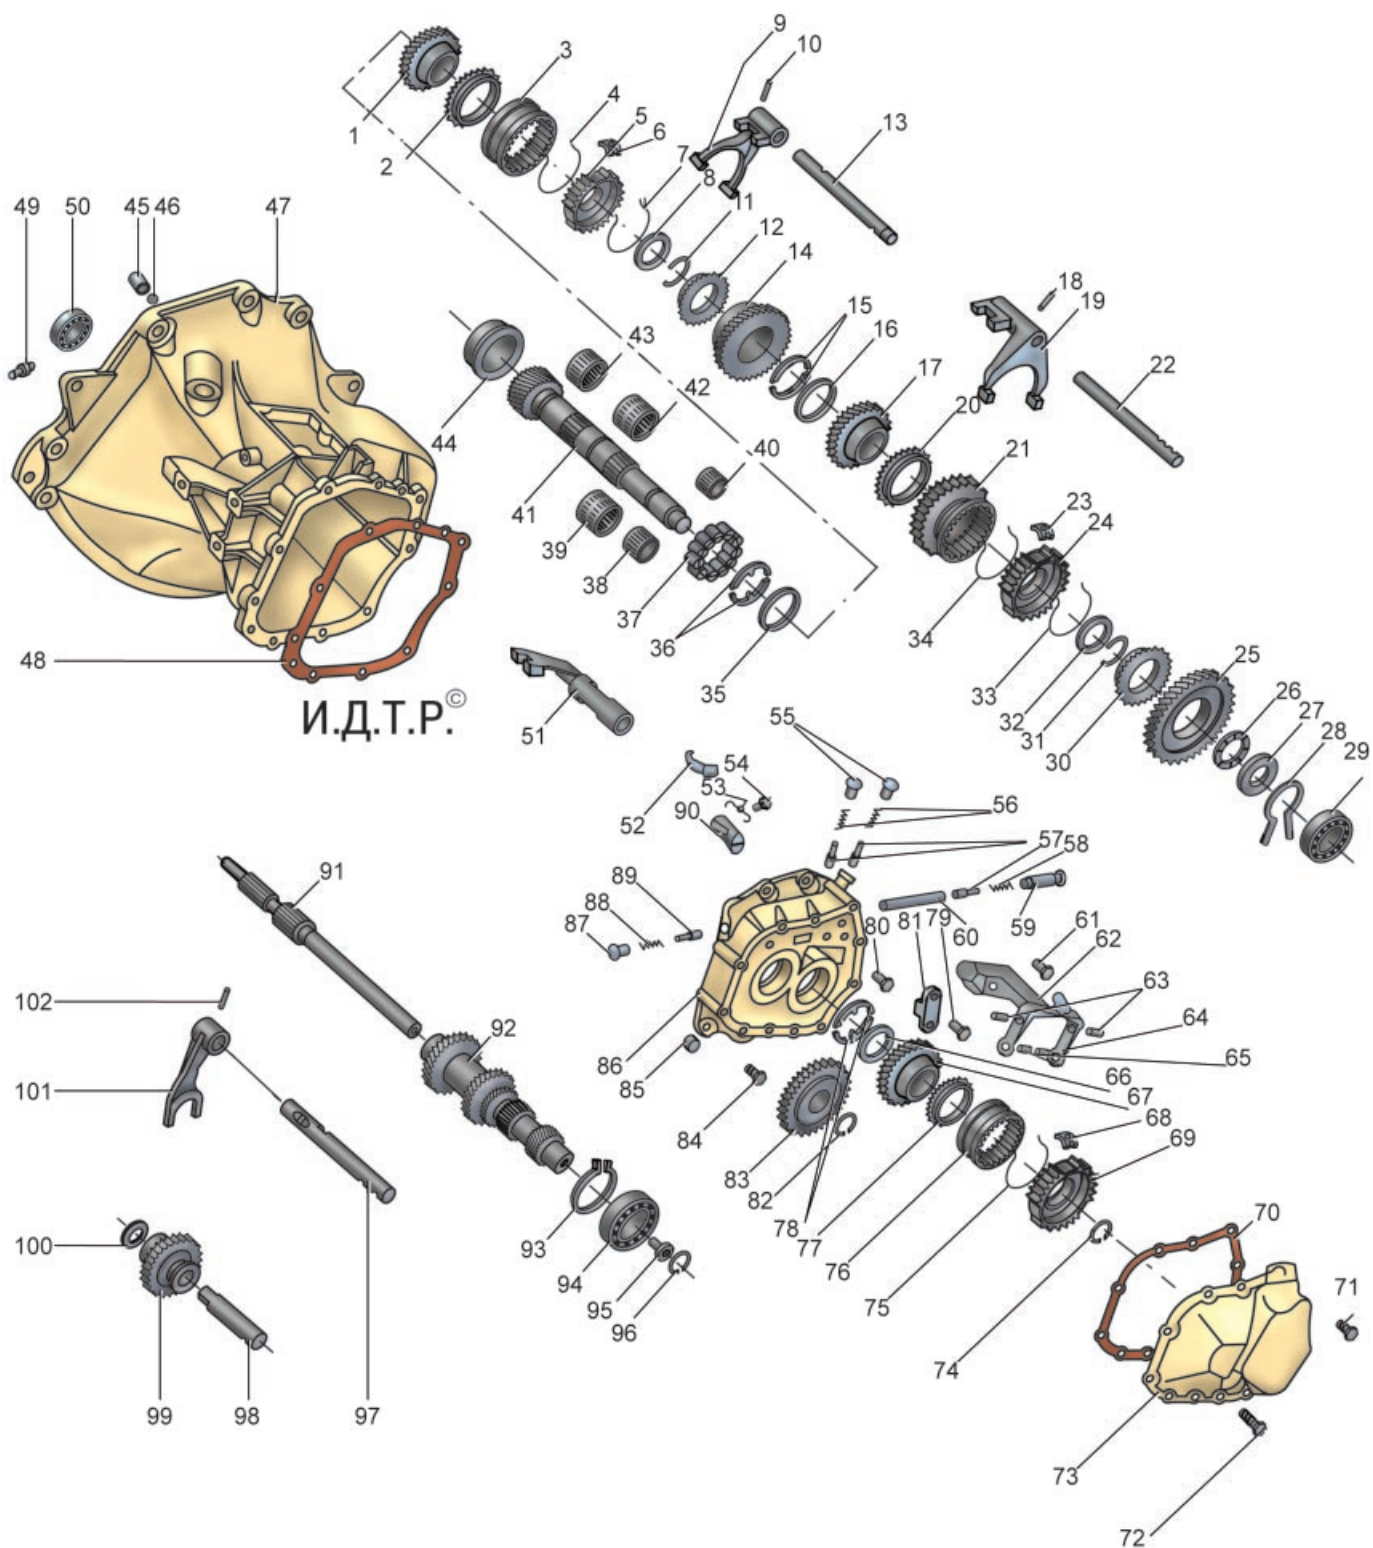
Детали механической коробки передач: 1 – шестерня IV передачи; 2, 12, 20, 30, 77 – блокирующие кольца синхронизаторов; 3 – муфта включения синхронизатора III и IV передач; 4, 7, 33, 34, 75 – пружинные кольца синхронизаторов; 5 – ступица синхронизатора III и IV передач; 6, 23, 68 – сухари синхронизаторов; 8, 32 – упорные шайбы; 9 – вилка переключения III и IV передач; 10, 18, 102 – штифты; 11, 31, 74, 82, 93, 96 – стопорные кольца; 13 – шток вилки переключения III и IV передач; 14 – шестерня III передачи; 15, 36, 78 – упорные полукольца; 16, 35, 66 – запорные кольца; 17 – шестерня II передачи; 19 – вилка переключения I и II передач; 21 – муфта включения синхронизатора I и II передач; 22 – шток вилки переключения I и II передач; 24 – ступица синхронизатора I и II передач; 25 – шестерня I передачи; 26 – упорный игольчатый подшипник шестерни I передачи; 27 – опорная шайба; 28 – пружинное кольцо; 29 – подшипник вторичного вала; 37 – роликовый подшипник вторичного вала; 38 – игольчатый подшипник шестерни I передачи; 39 – игольчатый подшипник шестерни II передачи; 40 – игольчатый подшипник шестерни V передачи; 41 – вторичный вал; 42 – игольчатый подшипник шестерни III передачи; 43 – игольчатый подшипник шестерни IV передачи; 44 – наружное кольцо роликового подшипника вторичного вала; 45 – пробка; 46 – магнит; 47 – картер коробки передач; 48 – прокладка картера сцепления; 49 – выключатель фонарей света заднего хода; 50 – роликовый подшипник первичного вала; 51 – поводок со штоком V передачи; 52 – собачка; 53 – пружина собачки; 54, 61, 71, 72, 79, 81, 84 – болты; 55, 59, 87 – пробки фиксаторов; 56, 58, 88 – пружины; 57, 89 – фиксаторы; 60 – штифт механизма блокировки; 62 – кронштейн вилки включения V передачи; 63 – ось вилки включения V передачи; 64 – вилка включения V передачи; 65 – сухари вилок; 67 – ведомая шестерня V передачи; 69 – ступица синхронизатора V передачи; 70 – прокладка крышки; 73 – задняя крышка коробки передач; 76 – муфта включения синхронизатора V передачи; 80 – кронштейн собачки; 83 – ведущая шестерня V передачи; 85 – магнит; 86 – промежуточный картер; 90 – кронштейн собачки; 91 – первичный вал; 92 – блок шестерен; 94 – шариковый подшипник блока шестерен; 95 – винт; 97 – шток вилки включения промежуточной шестерни заднего хода; 98 – ось промежуточной шестерни заднего хода; 99 – промежуточная шестерня заднего хода; 100 – шайба; 101 – вилка включения промежуточной шестерни заднего хода
